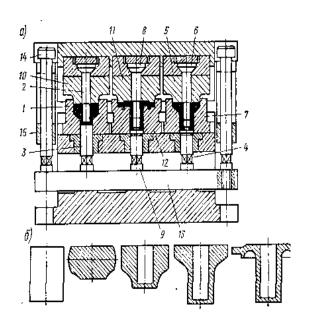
Схема штампа для выдавливания полой поковки (а); на виде б показаны заготовка и поковки по переходам штамповки: 1, 7, 12 — матрицы; 2, 6, 8 — прошивни; 3, 4, 9 — выталкиватели; 5, 10, 11 — пуансоны; 13 — траверса; 14 — тяга траверсы; 15 — направляющая втулка
